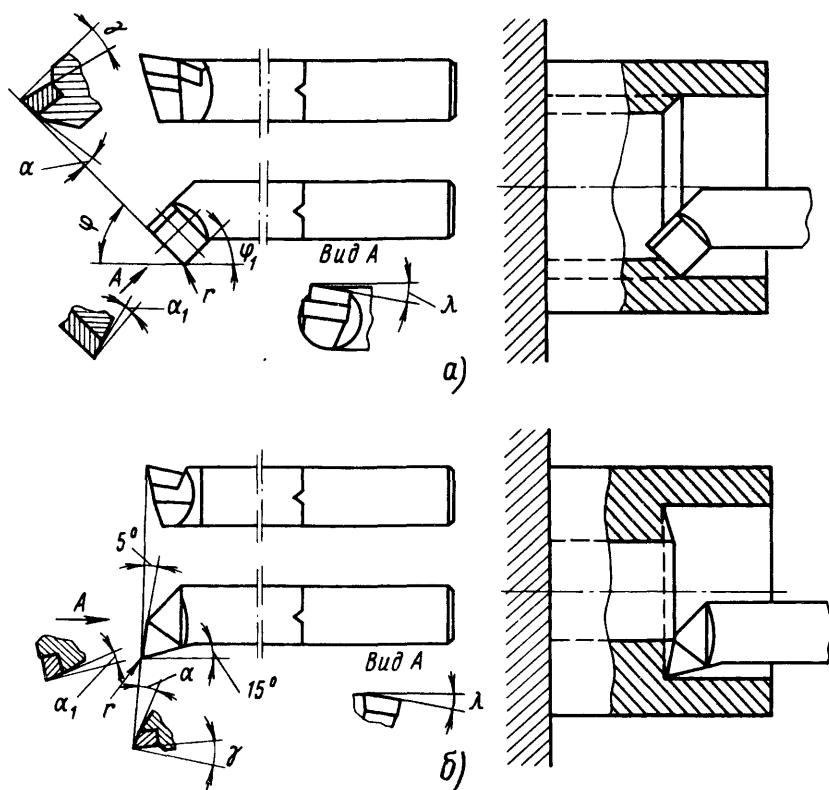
Токарные расточные резцы, оснащенные пластинками из твердого сплава для обработки сквозных (а) и глубоких (б) отверстий
